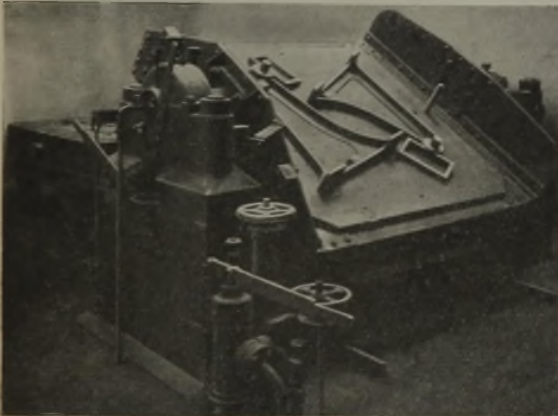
Gesamtansicht der Rüttelformmaschine.
